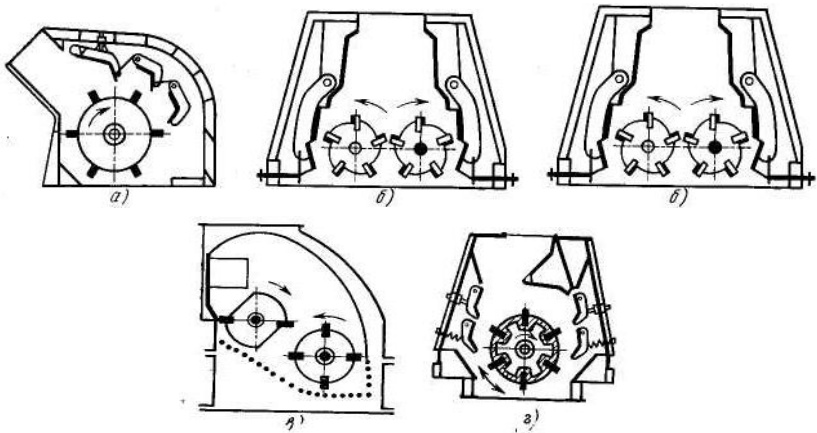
Основні конструктивні схеми роторних дробарок:
